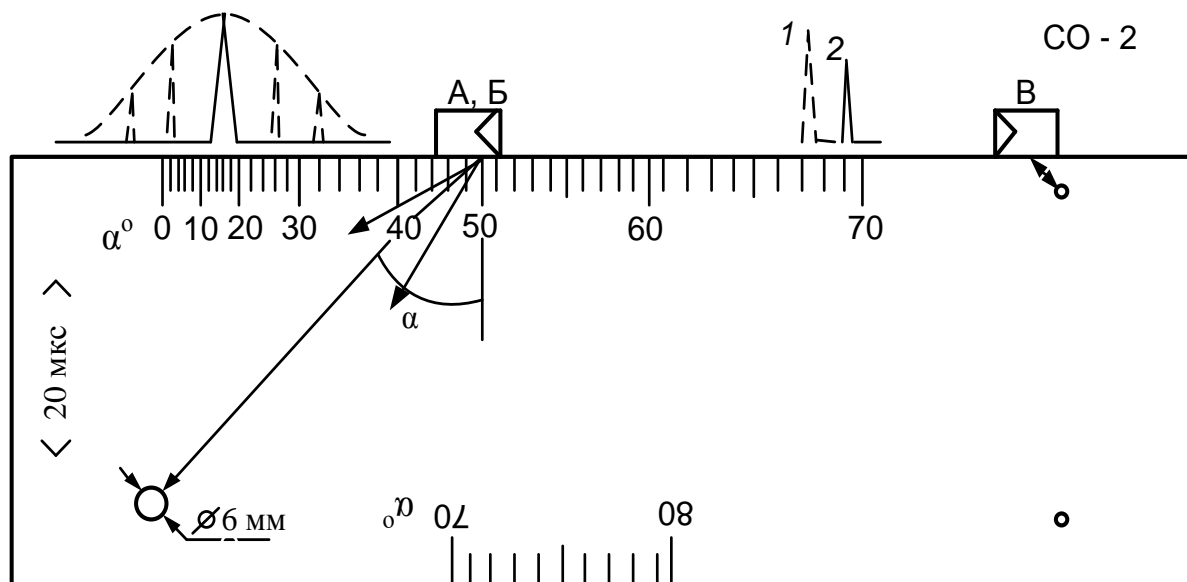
Стандартный образец СО-2 (ГОСТ 14782-86):
